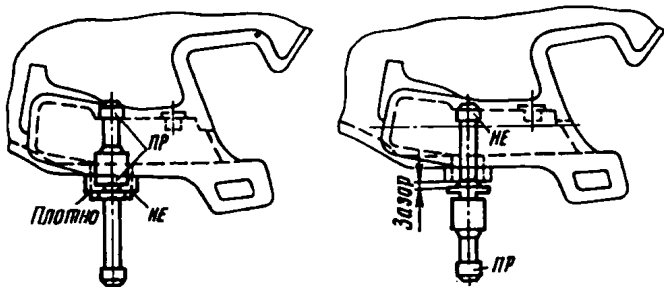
Проверка диаметров и соосности малого и большого отверстий для валика подъемника в корпусе автосцепки шаблоном 797р
